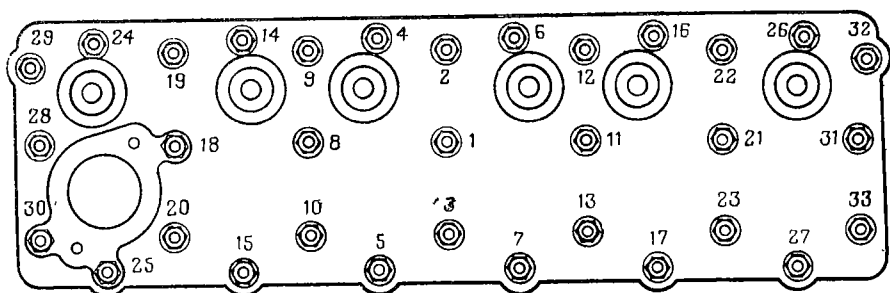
Последовательность затяжки гаек шпилек головки блока цилиндров:
